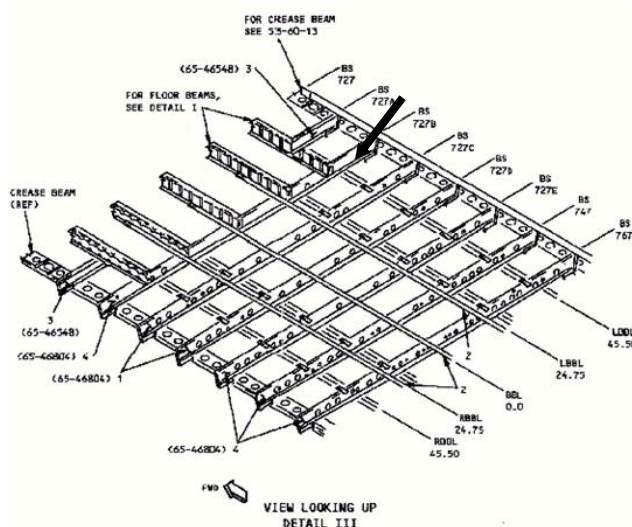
Retak pada struktur *Longitudinal Floor Beam* di bagian *Section 46*, (Sumber: PT. Garuda Maintenance Facility, Engineering Services, Unit TE)
